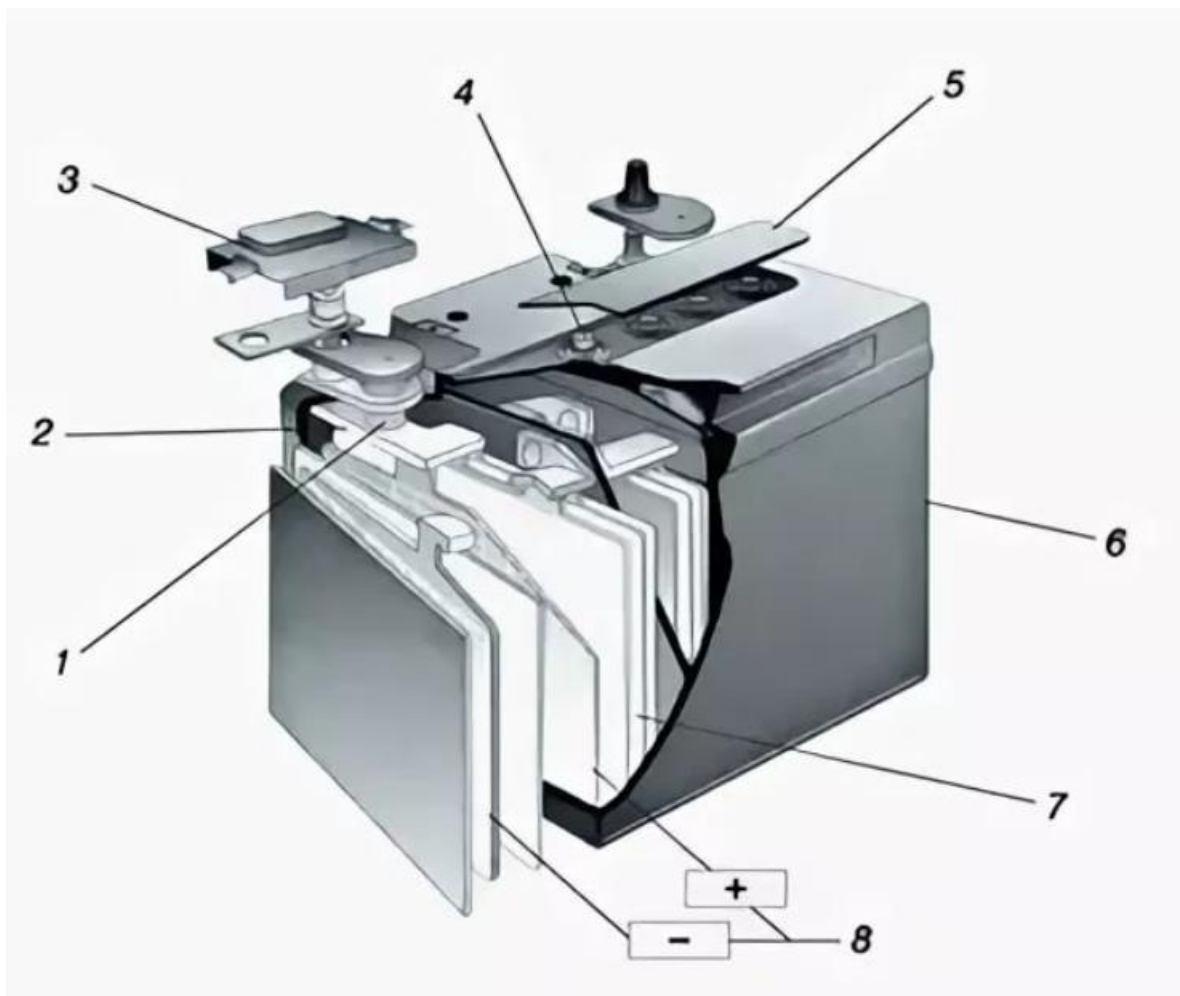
конструктивная схема AGM аккумуляторной батареи: 1 – уплотнительное кольцо вывода; 2 – положительный вывод; 3 – изолирующая крышка; 4 – клапан избыточного давления; 5 – крышка клапанов; 6 – корпус; 7 – стекловолоконный сепаратор; 8 – положительные и отрицательные пластины.
